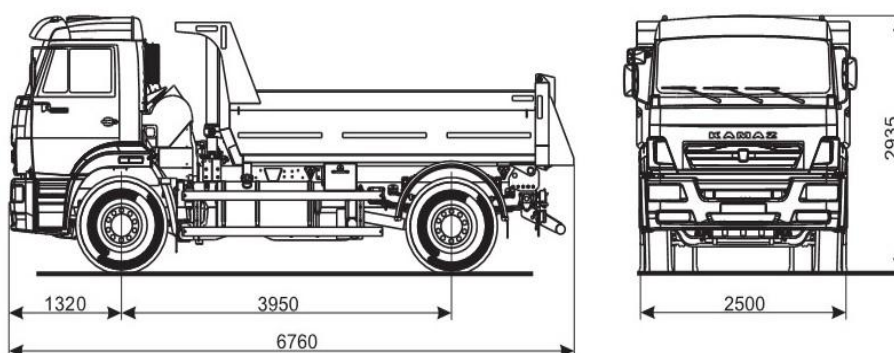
Общий вид автомобиля КамАЗ 53605
